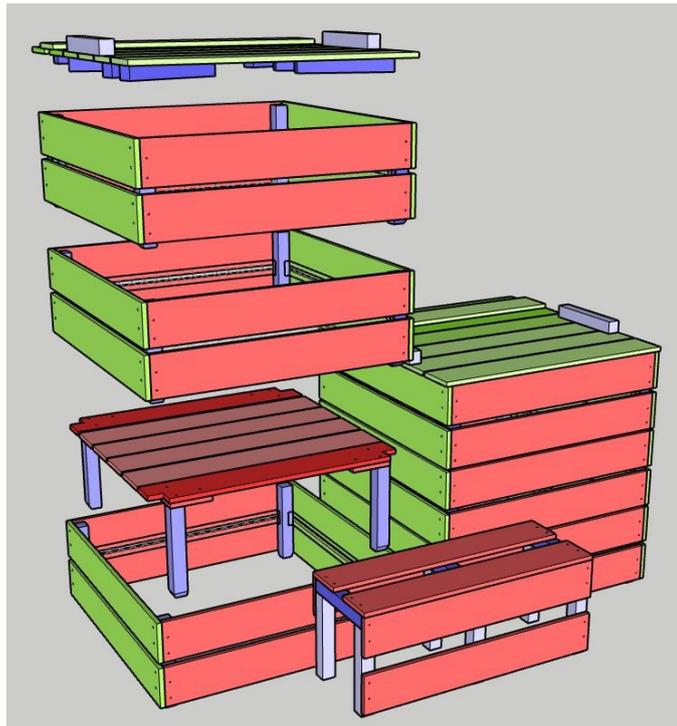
Vue d'ensemble du Compostou v3, avec éclaté du bloc à broyat
